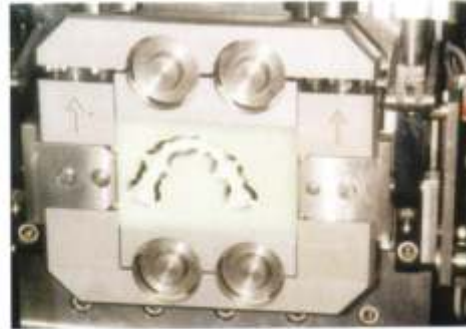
Aufnahmevorrichtung für die Materialblöcke, in der diese unter Wasserkühlung gefräst werden.
